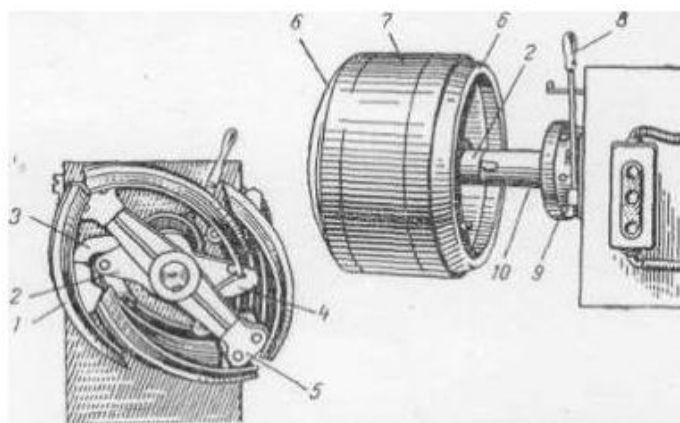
Жорсткий металевий напівплощинний барабан верстата для складання покриттів: 1 - сектор барабану; 2 - важільна муфта; 3,4 - важелі; 5 - хрестовина; 6 - плечики; 7 - корона; 8 - рукоятка гальма; 9 - гальмо; 10 - порожнистий вал
